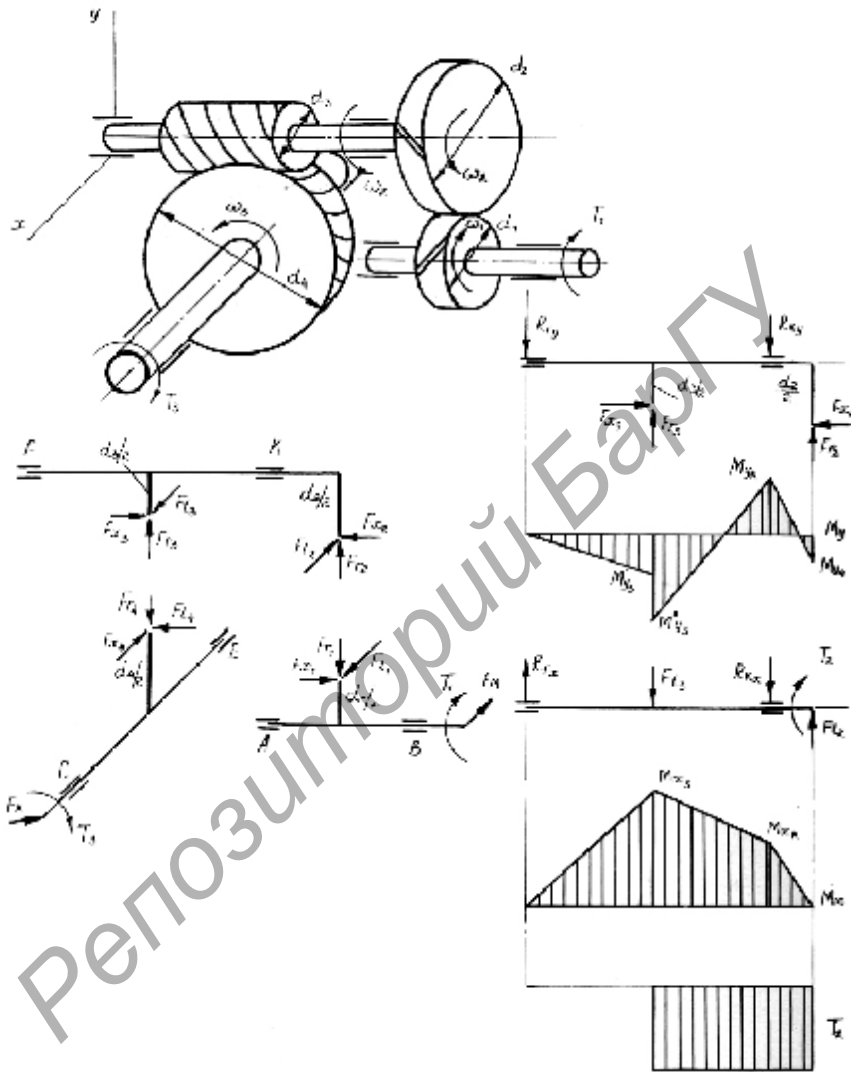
Зубчато-червячная передача с первой цилиндрической косоугольной ступенью
